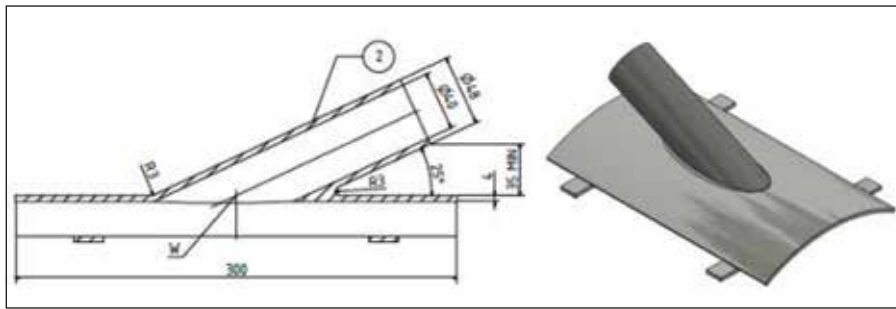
• Darstellung der genutzten Demonstratorgeometrie; links: technische Zeichnung, rechts: 3D Ansicht.
